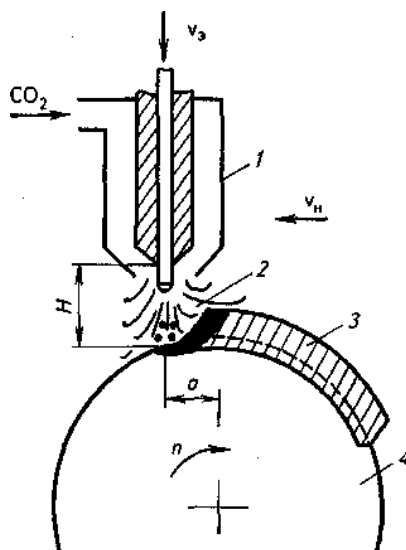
Схема наплавки в среде углекислого газа (1- наплавочная головка; 2 – зона подачи CO<sub>2</sub>; 3 – наплавленный металл; 4 – деталь)
